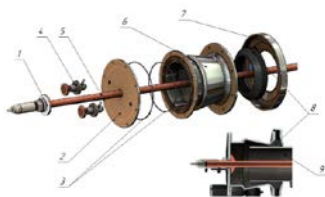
Конструктивные элементы фланца: 1 – токоввод; 2 – фланец-заглушка; 3 – уплотнительные кольца; 4 – натекатели; 5 – анод; 6 – прижимной фланец; 7 – ответный фланец; 8 – уплотнение; 9 – напыляемая труба
